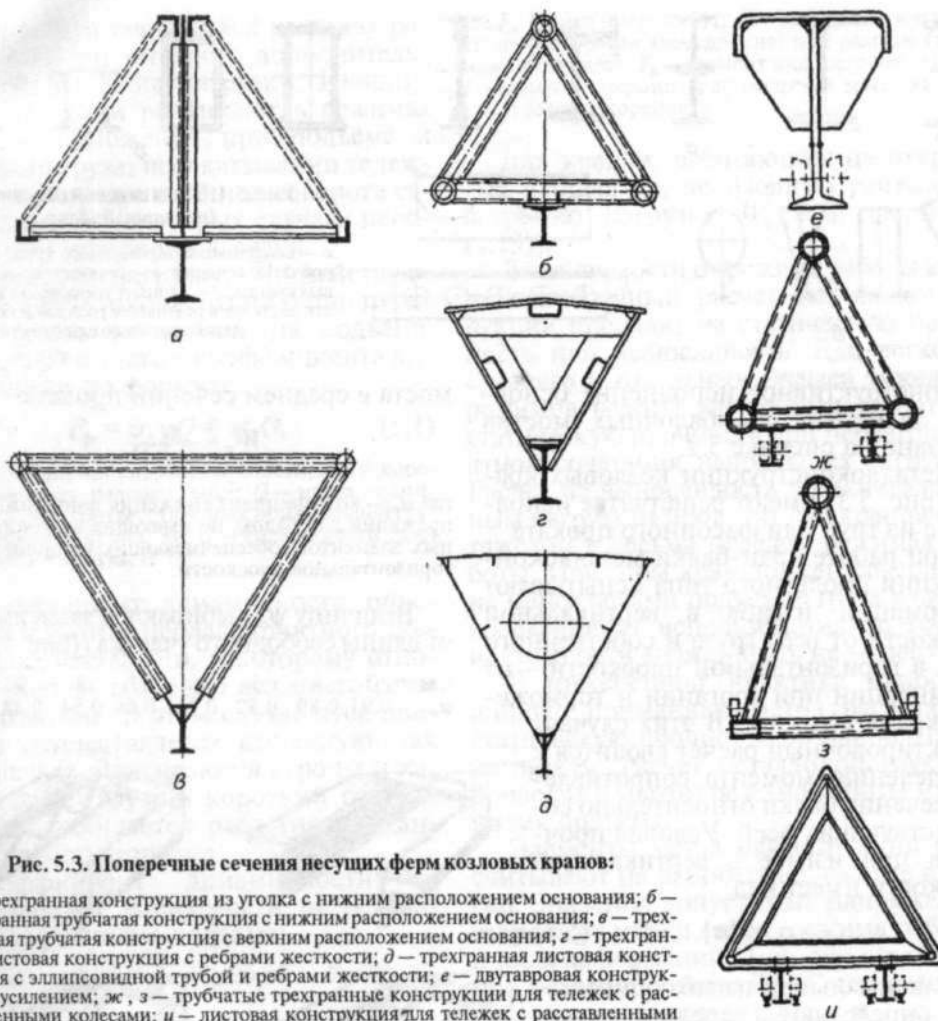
Поперечные сечения несущих ферм козловых кранов:
